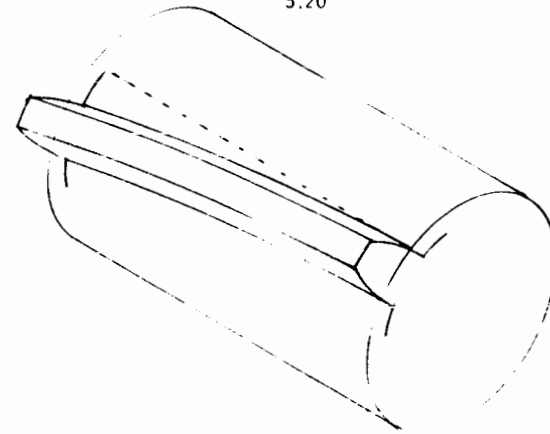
Perspectiva isométrica de un engrane cilíndrico de dientes helicoidales
